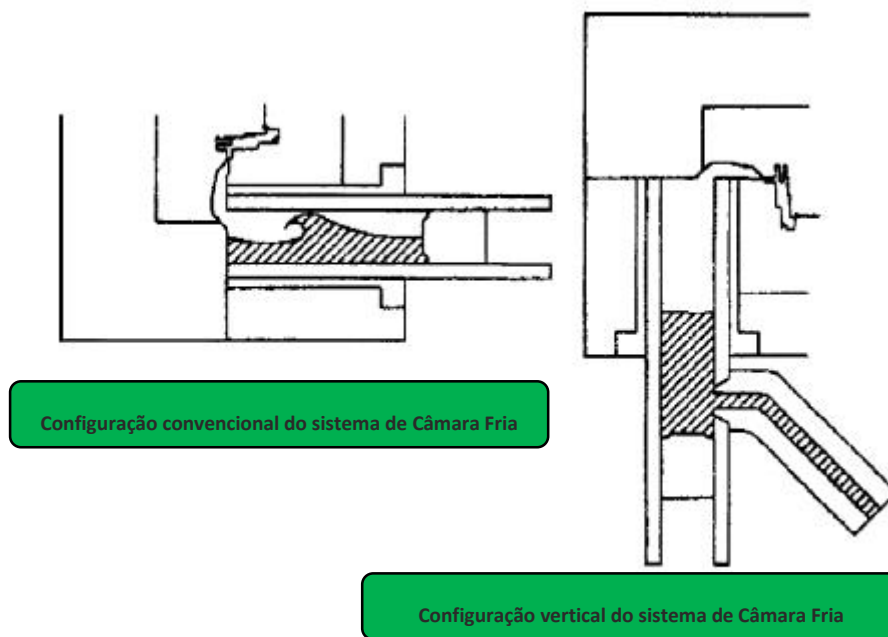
Configurações horizontal e vertical de máquinas de injeção de Câmara Fria (Die Cast Engineering [6])
